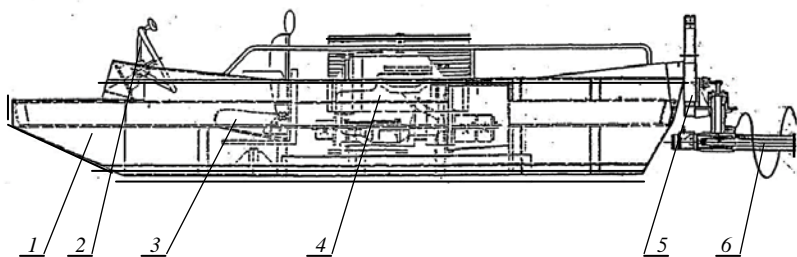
Мотобот с поворотным шнековым винтом: 1 – корпус; 2 – пост управления; 3 – сиденье оператора; 4 – силовая установка; 5 – поворотный редуктор; 6 – шнековый винт
